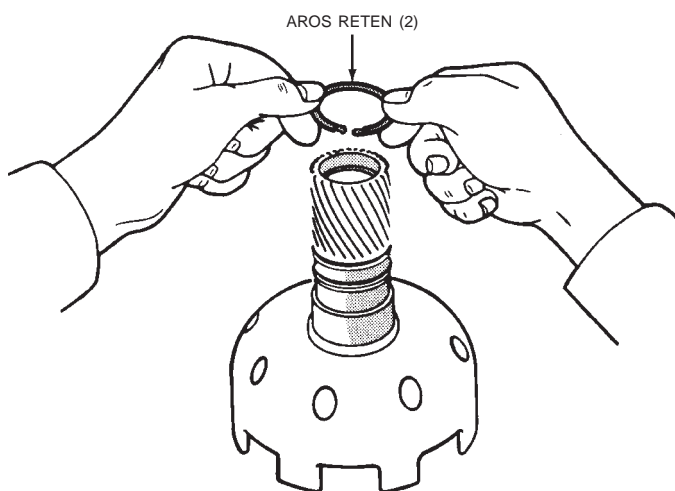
Desmontaje e instalación de los aros retén del engranaje solar
